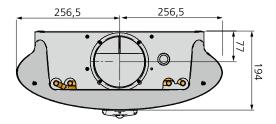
Dimensions ADRIATIC AWC Ellips, vue arrière du raccordement aéraulique
